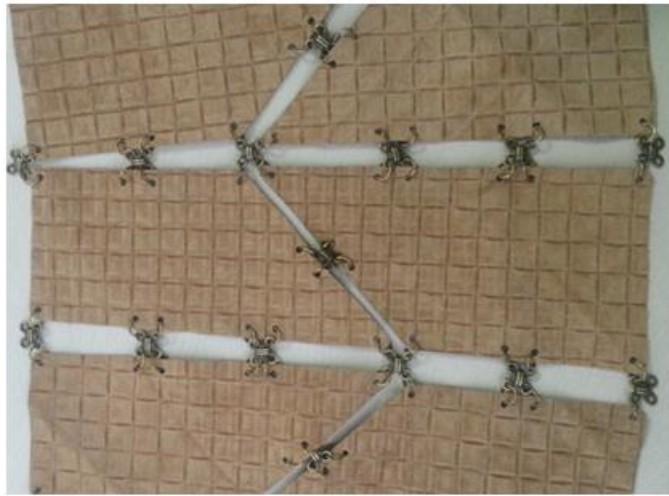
Детали конструкции, собранные в единую заготовку
